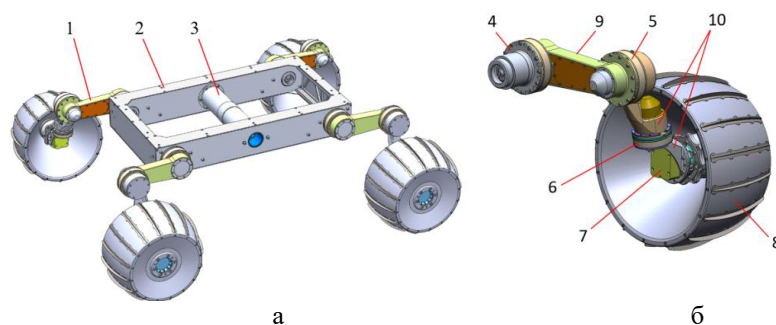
Общая конструктивная схема КШШ: 1 – ОДМ; 2 – рама; 3 – механизм синхронизации; 4 – привод бедра (ПБ); 5 – привод колена (ПК); 6 – привод поворота колеса (РП); 7 – тяговый привод колеса (ТП); 8 – колесо; 9 – рычаг бедра; 10 – рычаг голени
